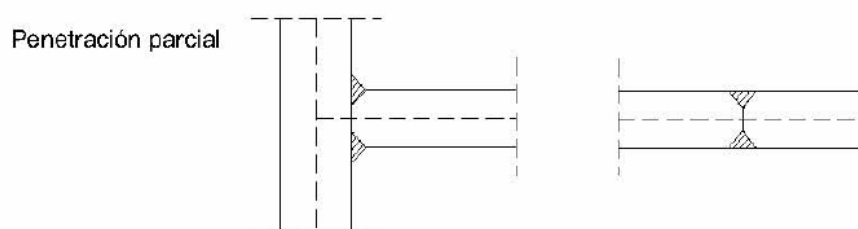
Penetración parcial de soldaduras a tope.
